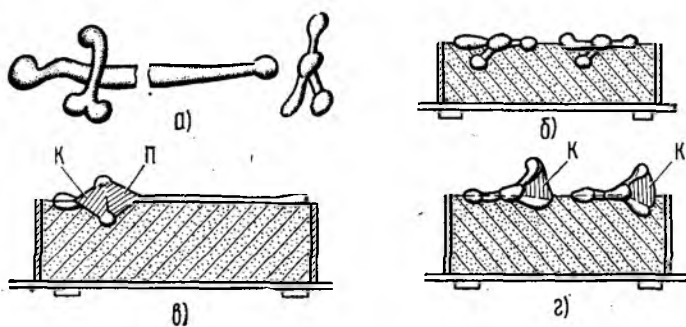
Процесс формовки шпaги к статуэтке «Мефистофель»
